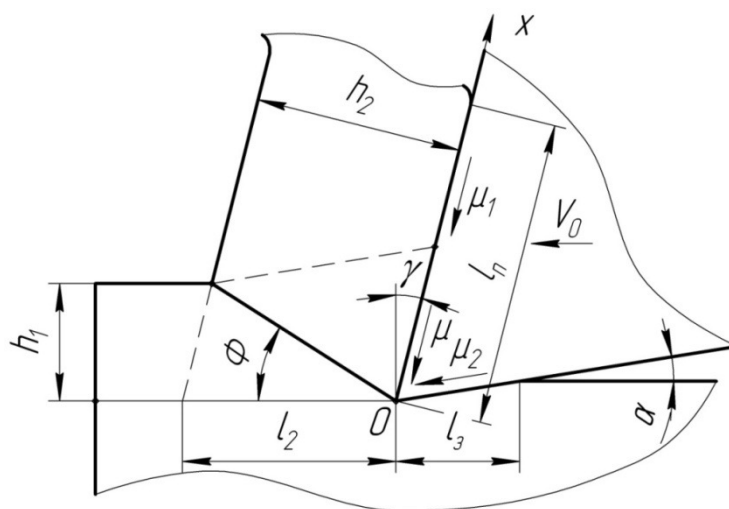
Схема контакта режущего клина с заготовкой, стружкой и обработанной поверхностью
